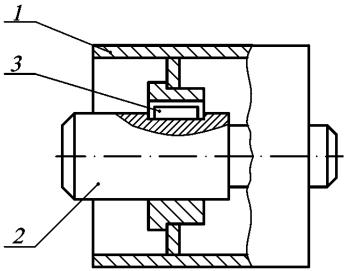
Сборочный чертеж со сварным корпусом: 1- корпус; 2- вал; 3- шпонка
